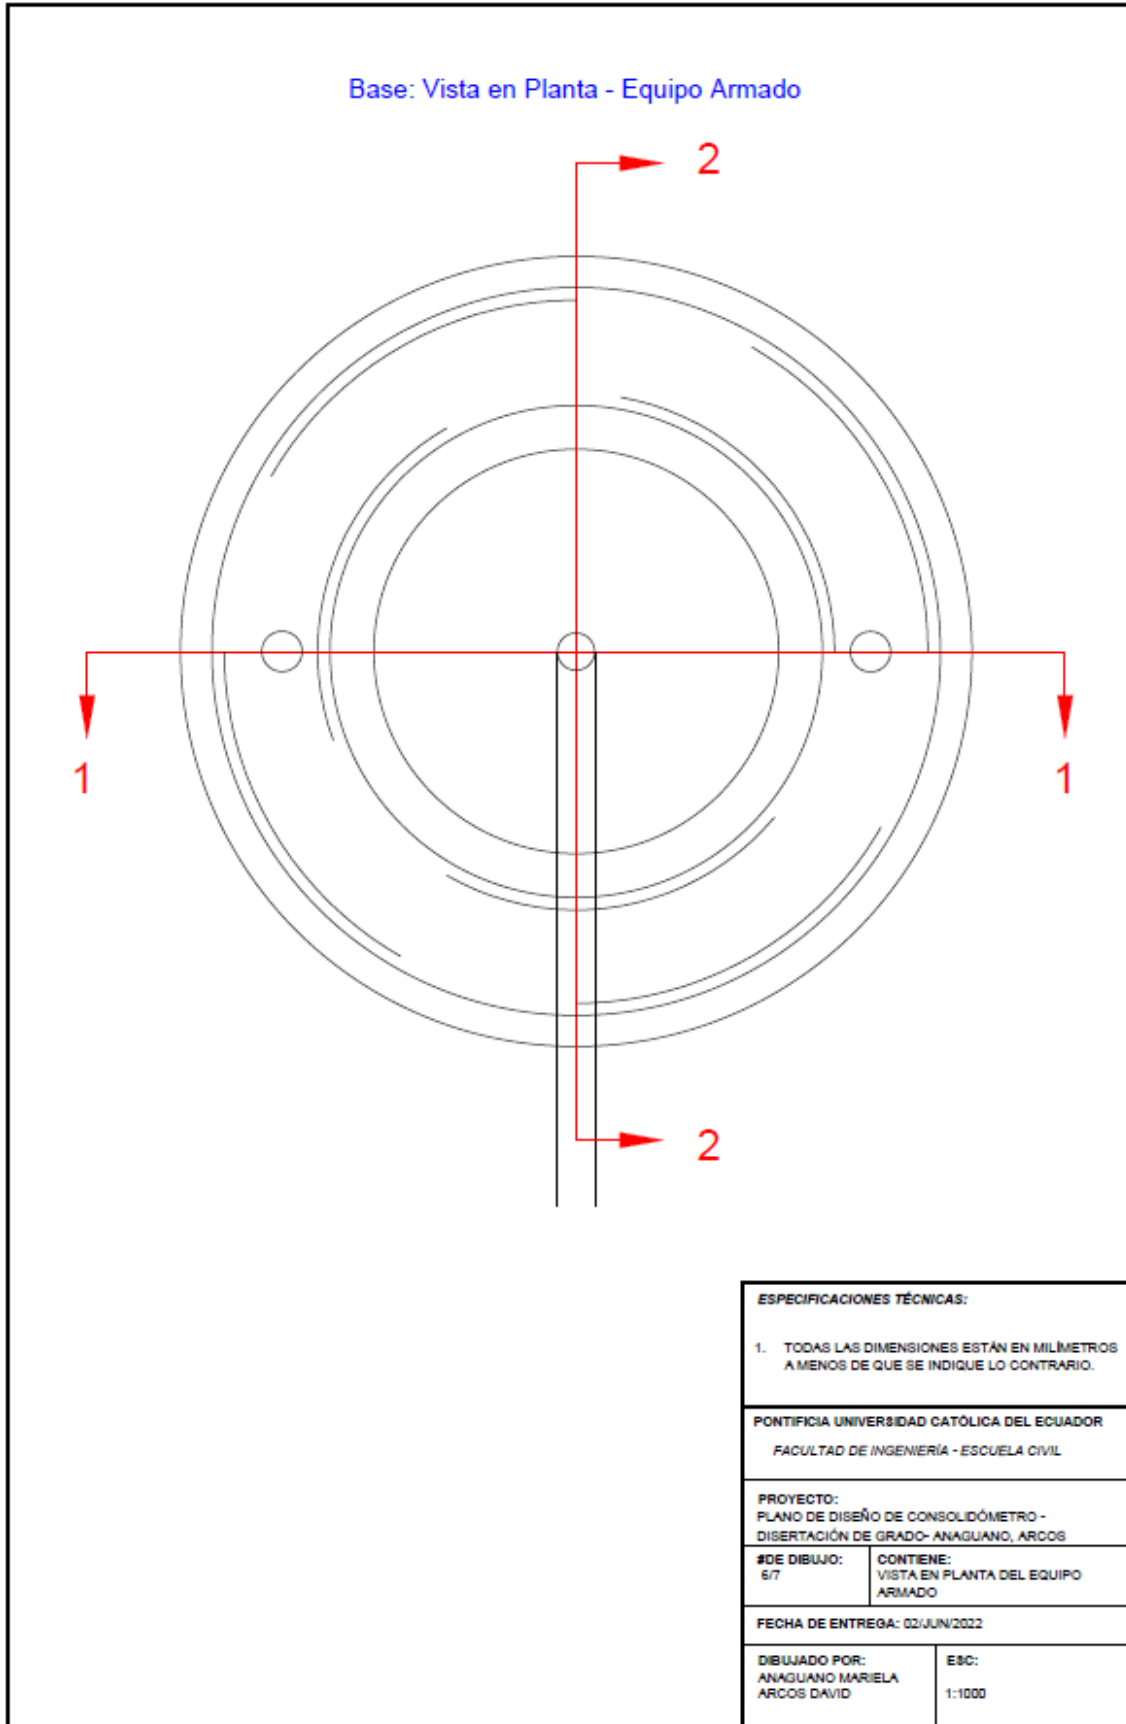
Plano de diseño del consolidómetro. Vista en planta del equipo armado. Elaboración propia.
